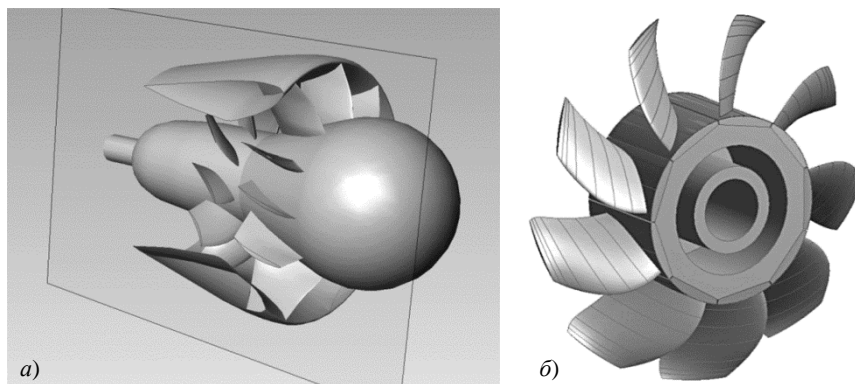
Конструкция а) водометного движителя и б) рабочего колеса
